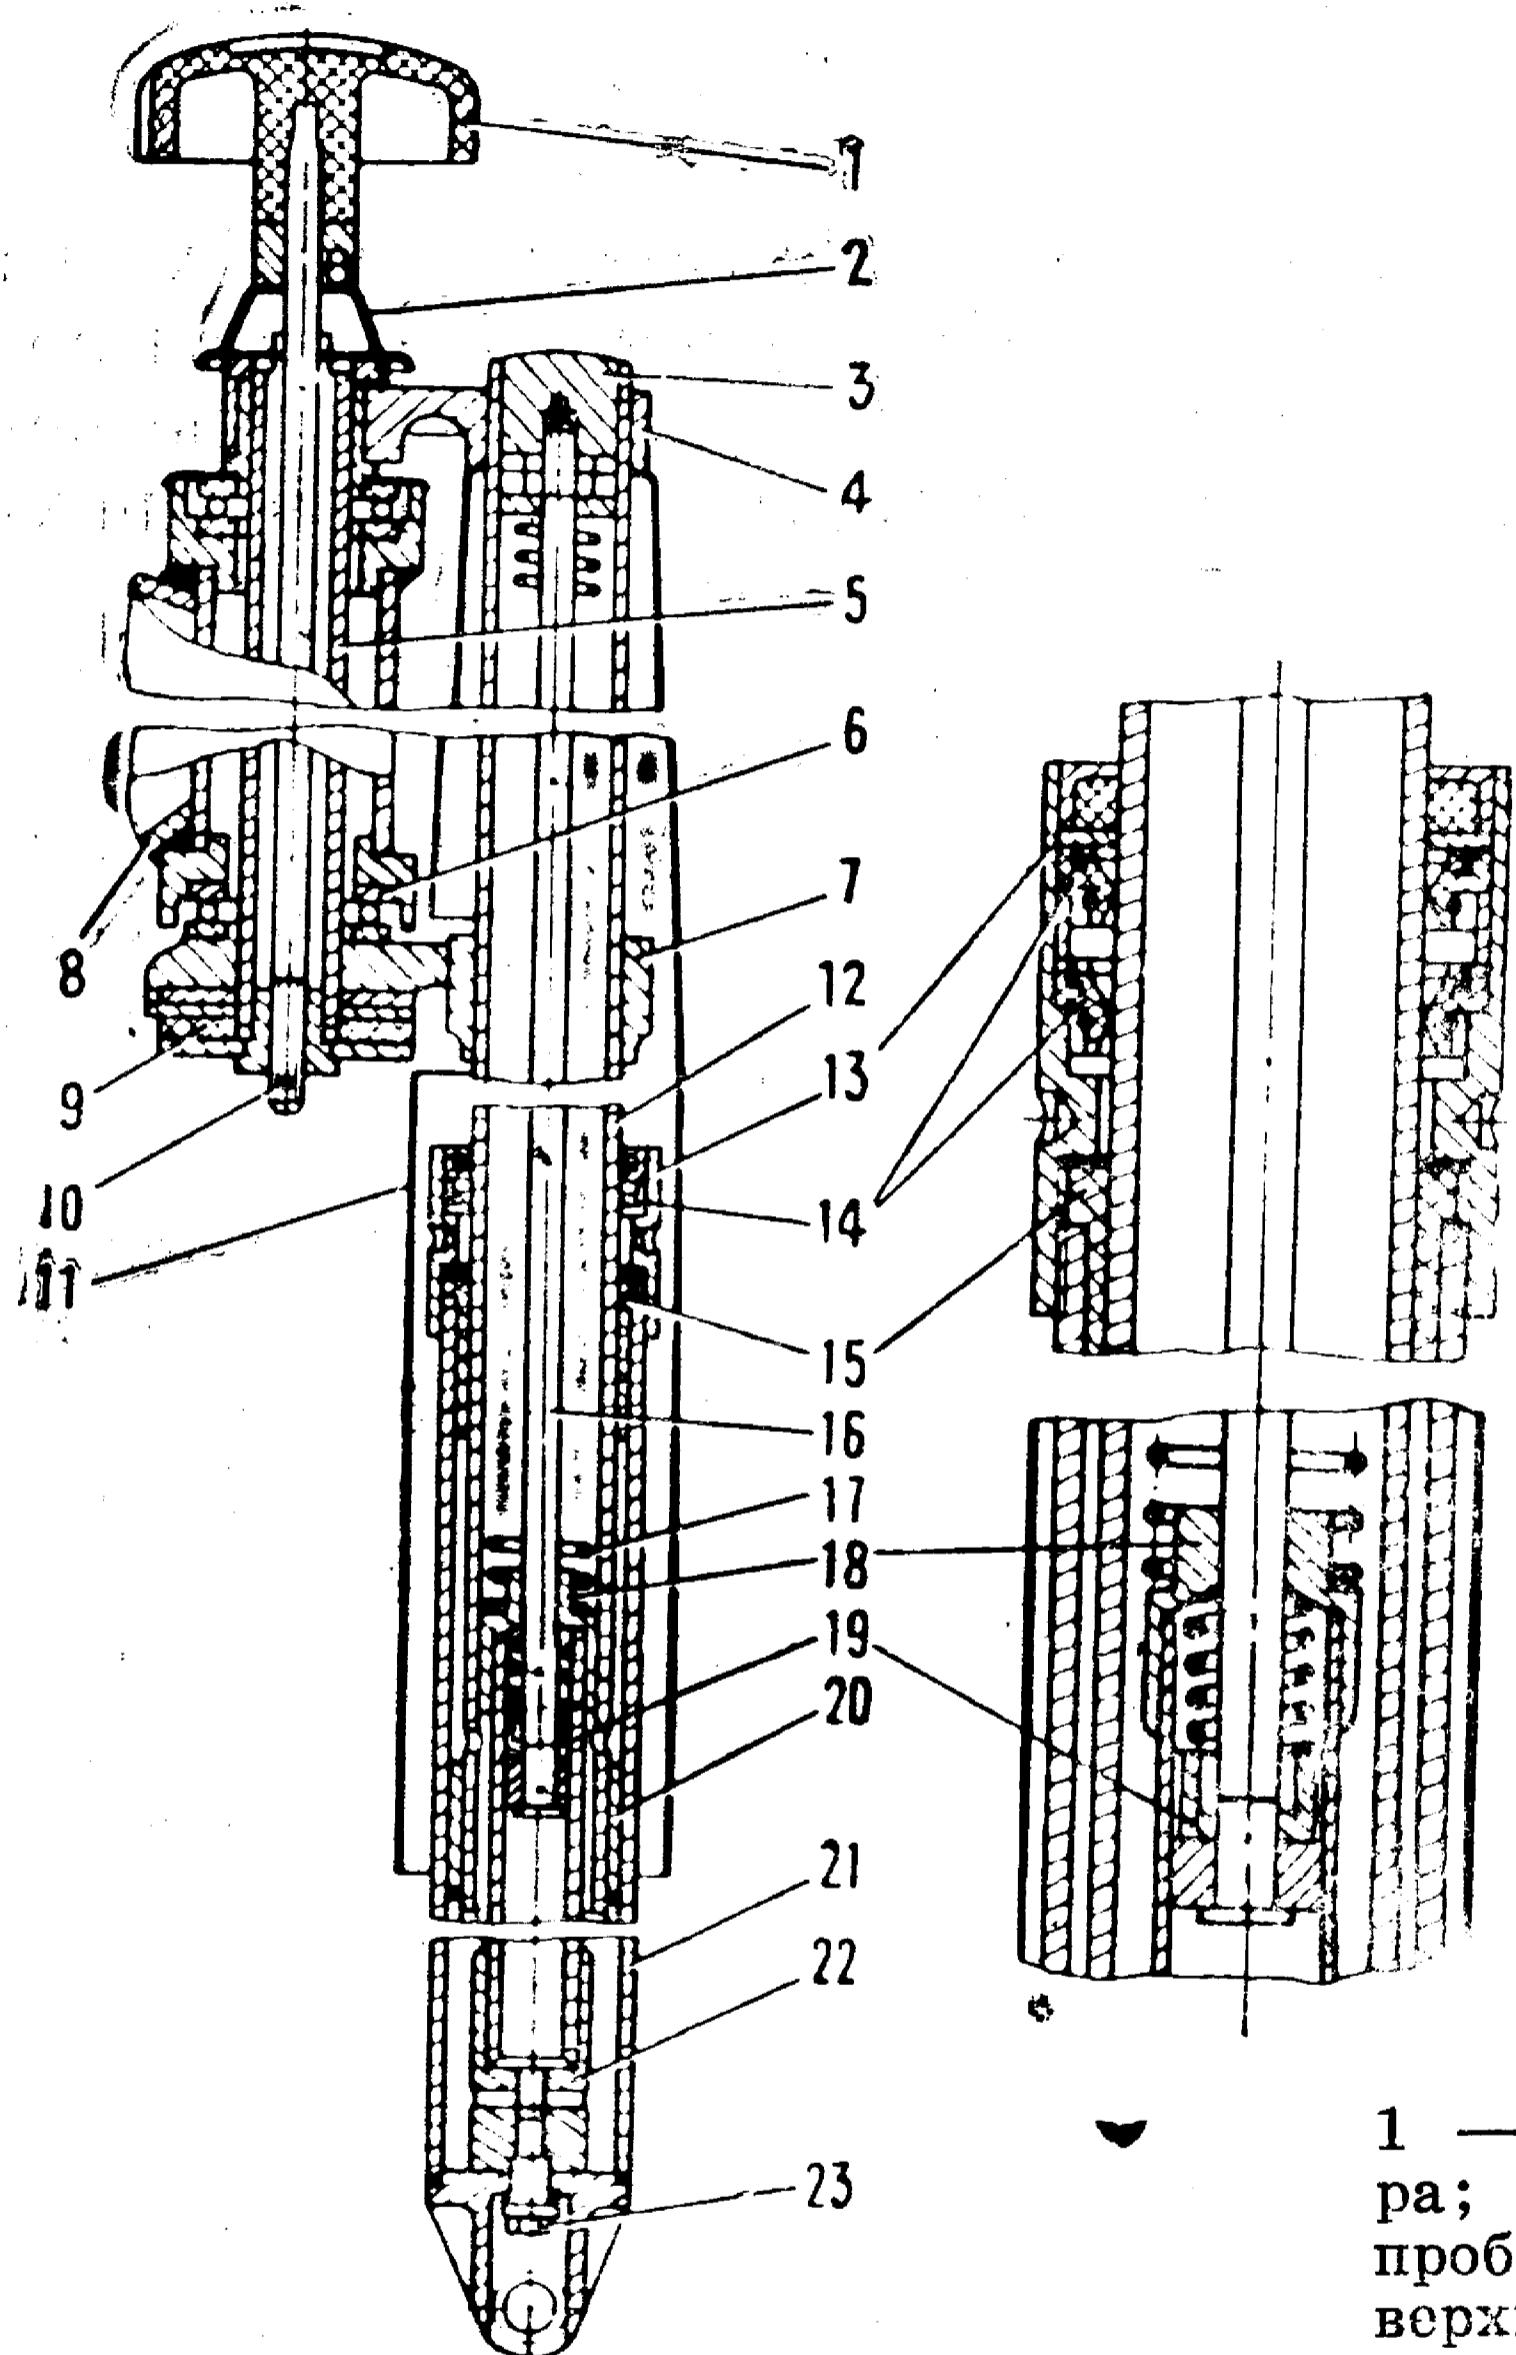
Подвеска переднего колеса с двухкулачковым тормозом:
